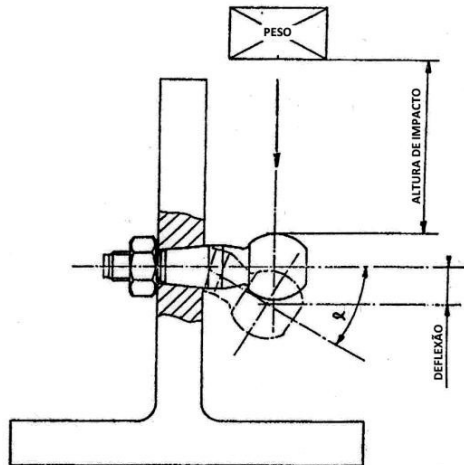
Esquema de montagem do ensaio de impacto de pino esférico do conjunto terminal de direção.
